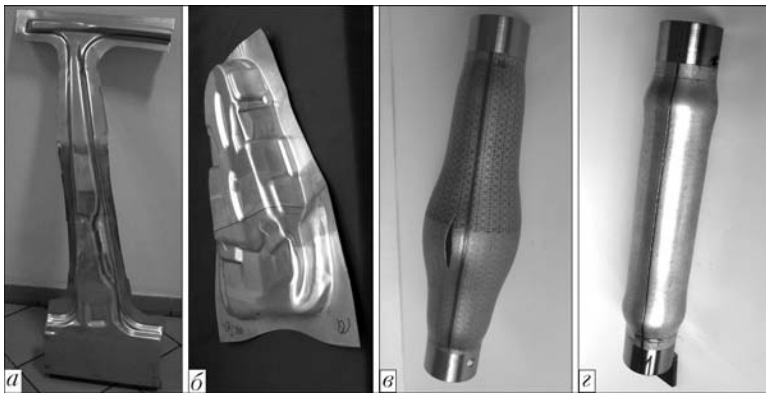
Заготовки с заданными свойствами и трубчатые заготовки, сваренные лазером: а, б — система: Lasercell TLC 1005, $f = 270$ мм. Материал — H180LAD. FeE 275 F ZNT/7,5/2 с; стандарт: FIAT; лазер мощностью 3800 Вт, защитный газ — гелий; в, г — система: ИАГ лазер HL 2006D/LCU, $f = 200$ мм
